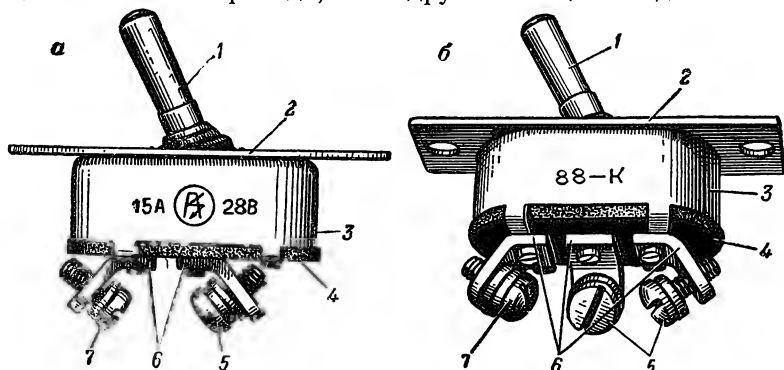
Общий вид выключателя 87-К и переключателя 88-К:
